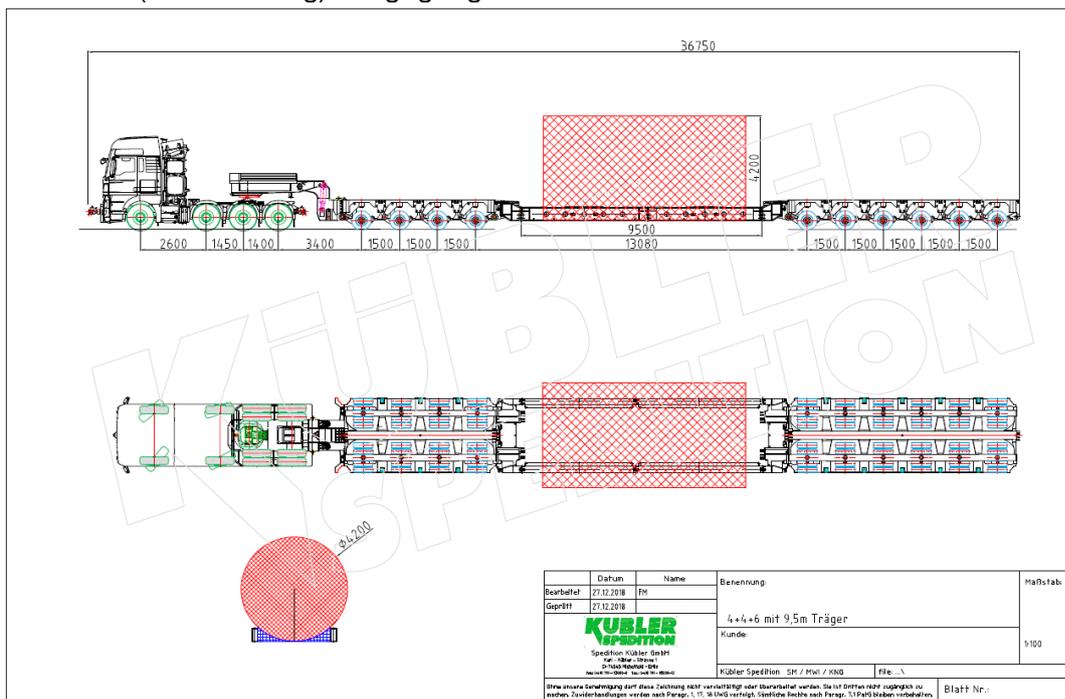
Kesselbrücke (beispielhaft Fa. Kübler)
